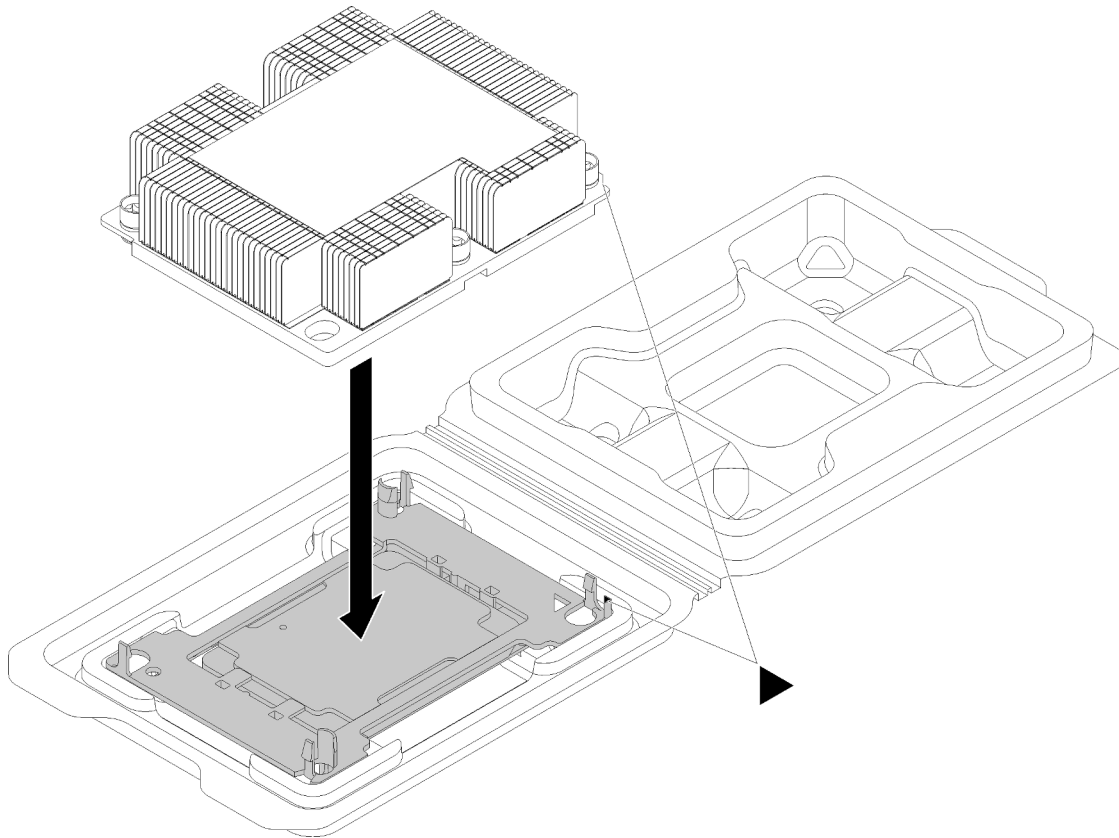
Assembler un module de processeur-dissipateur thermique dans le bac de transport
